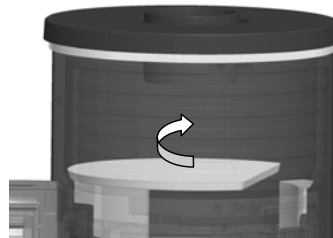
Uspořádání vedení plynu v kamnech zobrazení v řezu
